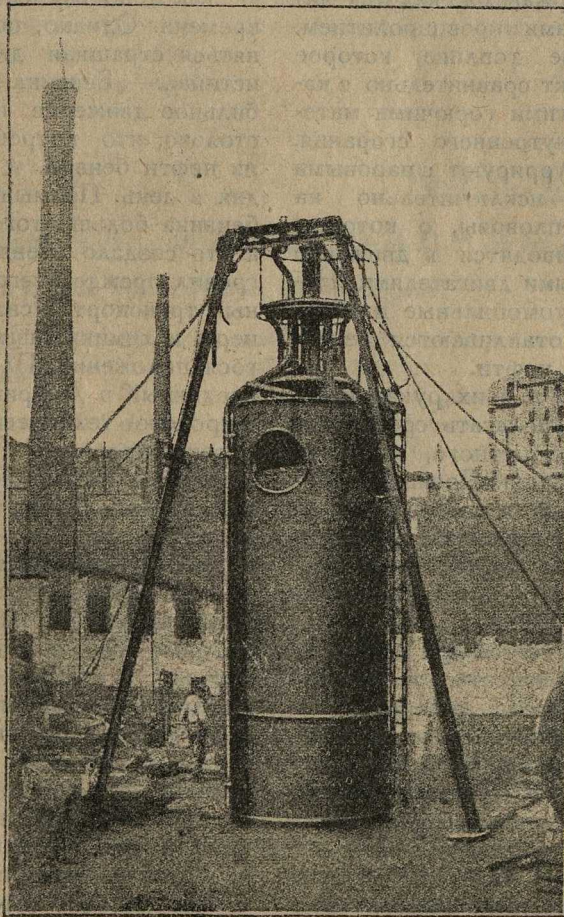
Внешний вид строящегося волнового двигателя с поплавокми.
